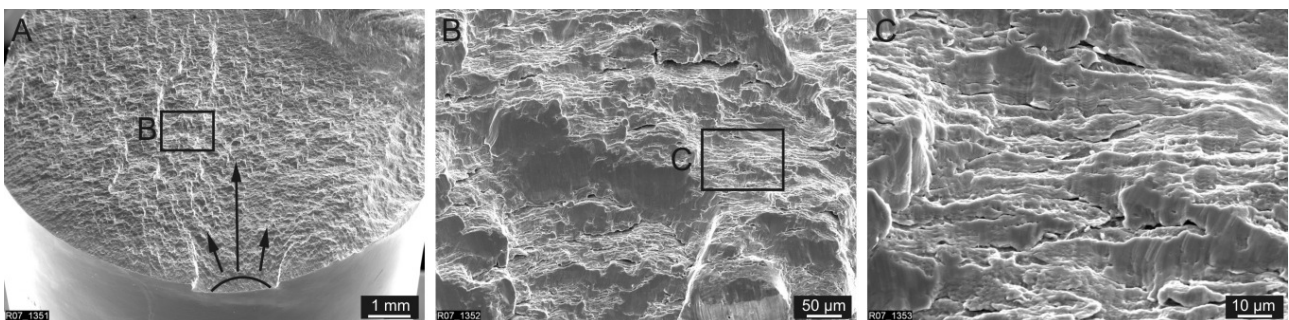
Rissausgang Ausschnitt B aus Bruchfläche Detail C, Schwingstreifen
